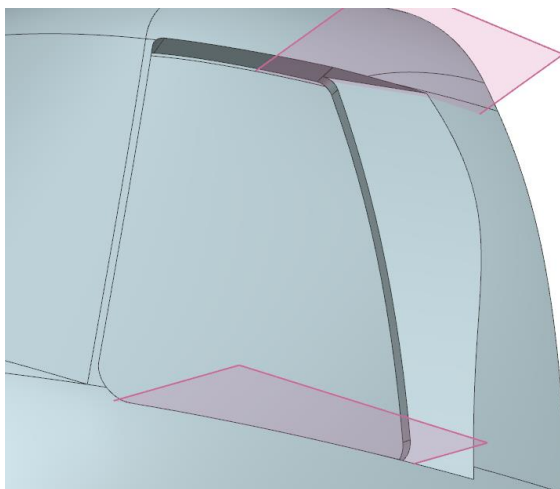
Проем для блистера сдвижного с поверхностью смещения
